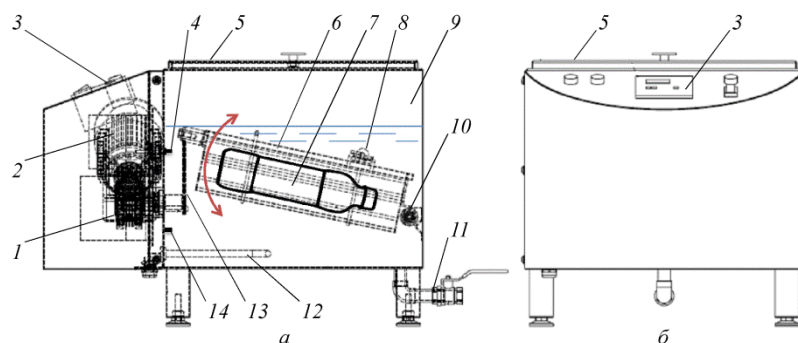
Устройство размораживателя молозива РМ-45 с качающейся корзиной:
